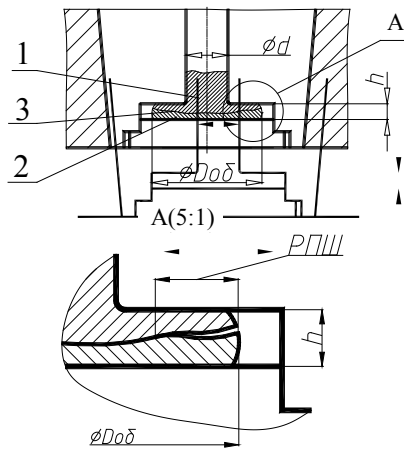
Схематическое представление стадии плакирования стержневых изделий: 1 — материал основы; 2 — плакирующий слой; 3 — сварной шов
